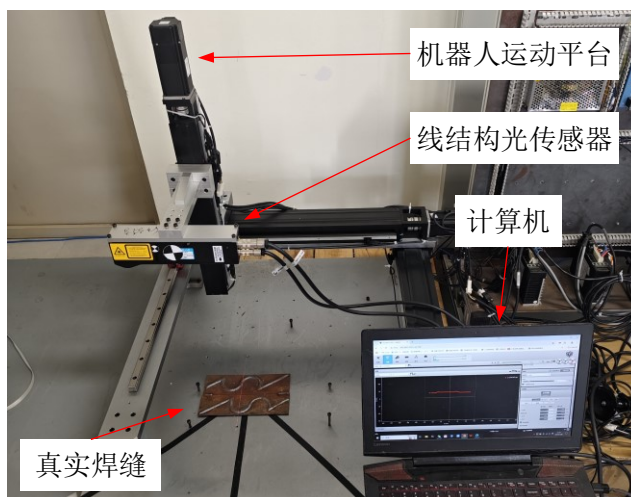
焊缝缺陷检测实验平台示意图
